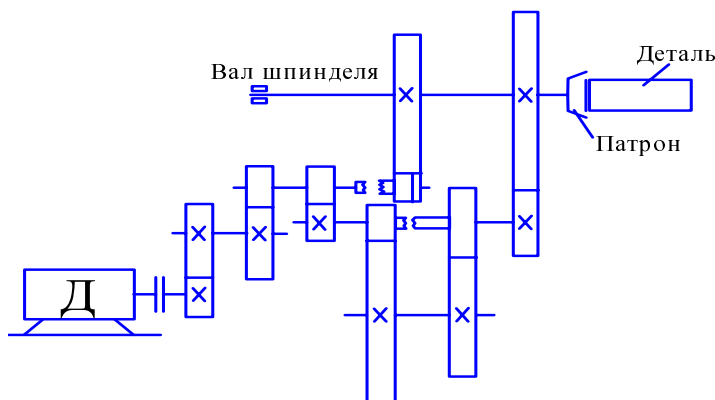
Кинематическая схема РЭП механизма главного движения токарного станка
